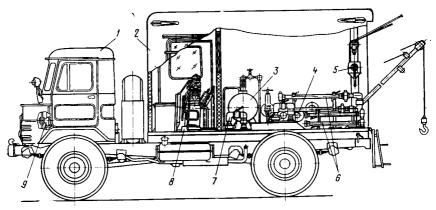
Блок арматуры дренажной очистки БАДО-210: i — автомобиль ГАЗ-66; 2 — кузов СГК-5Б; 3 — ресивер; 4 — пневмопривод; 5 — грузоподъемное устройство; 6 — трубы; 7 — шарнирные колена и переводники; 8 — компрессор; 9 — узел отключения насоса гидроусилителя руля
